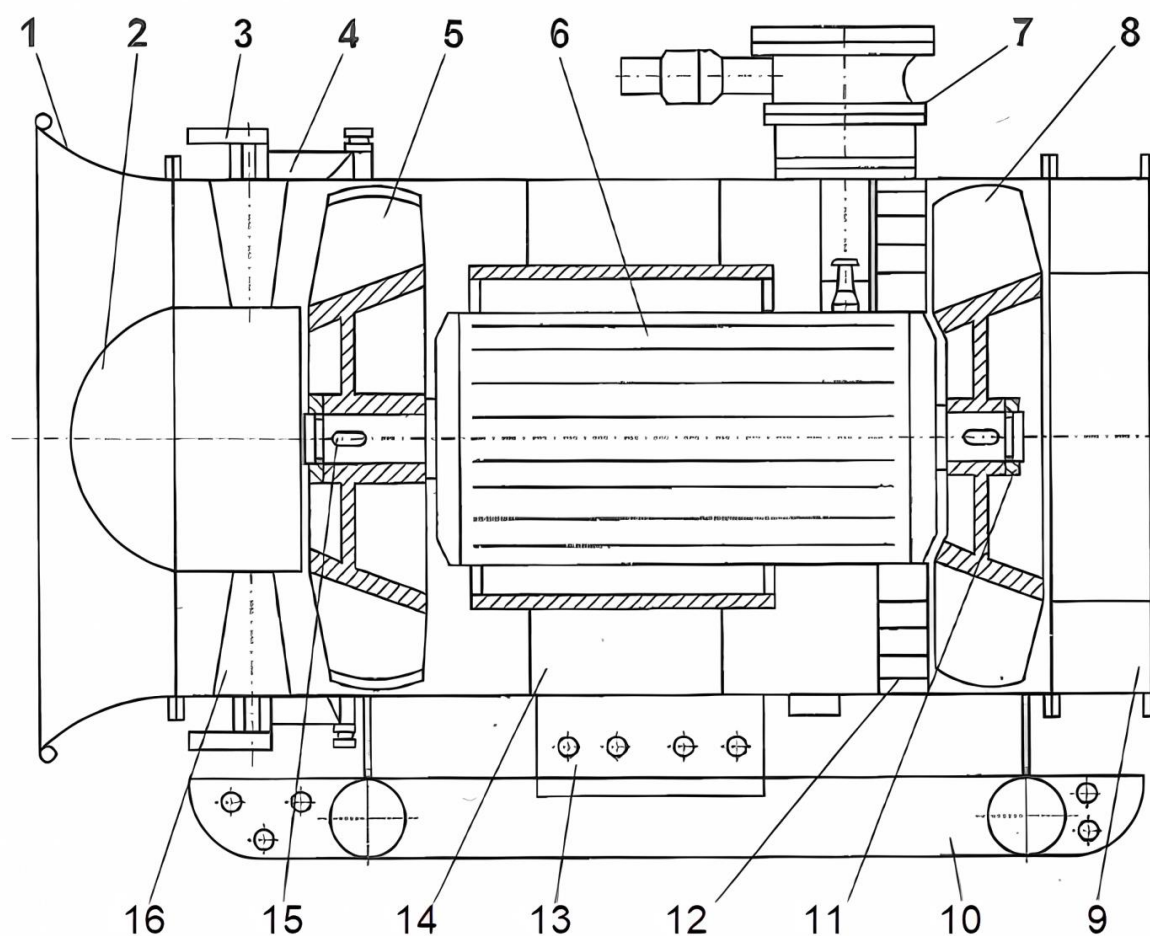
Вентилятор ВМЭ-2-10А: 1 – подвод (коллектор); 2 – передний обтекатель; 3 и 16 – привод и лопатки направляющего аппарата; 4 – противосрывное устройство; 5 и 8 – рабочие колеса 1-ой и 2-ой ступени; 6 – электродвигатель; 7 – ввод силового кабеля; 9 – отвод; 10 – салазки; 11 – стопорная гайка; 12 – жесткие лопатки \спрямляющего аппарата; 13 и 14 – опоры вентилятора и электродвигателя; 15 – шпонка
